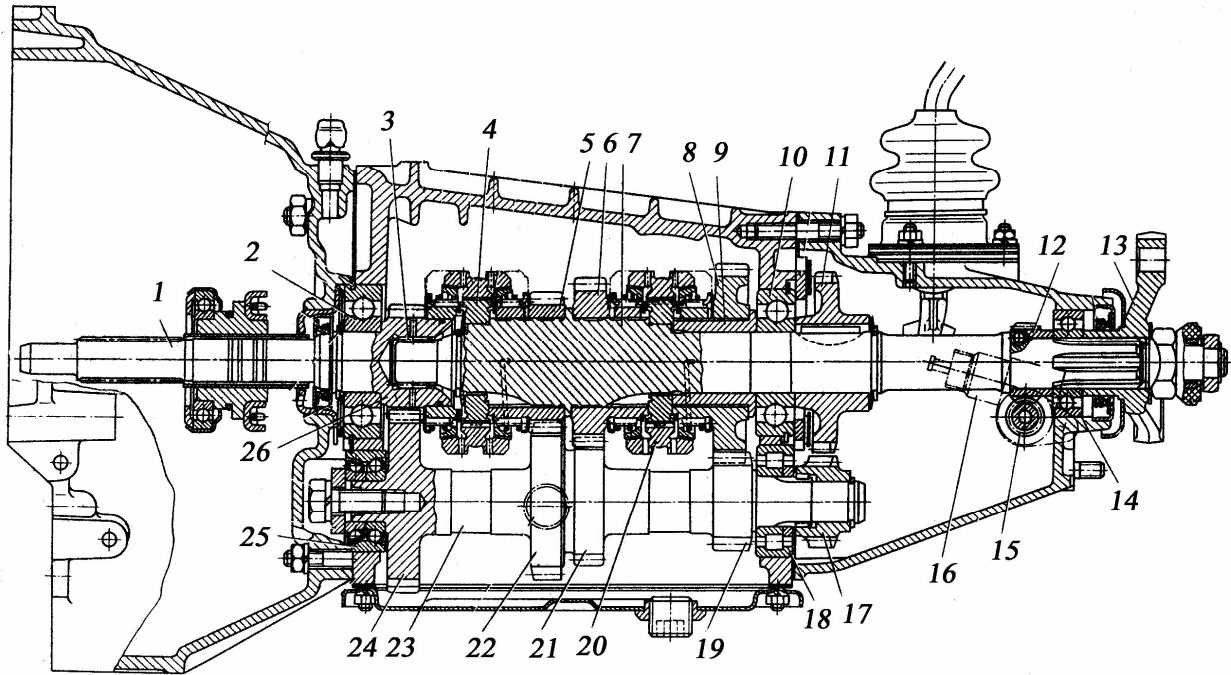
Трехвальная четырехступенчатая коробка передач автомобиля ВАЗ-2101
